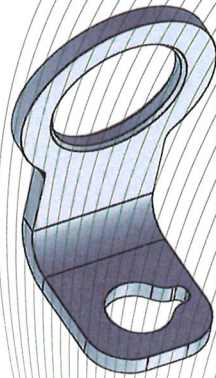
Kurvenhalterung, Typ: TS-Lasche (TS-011) (mit Sollbruchstelle, mit 45° Fase oder ohne Fase)
